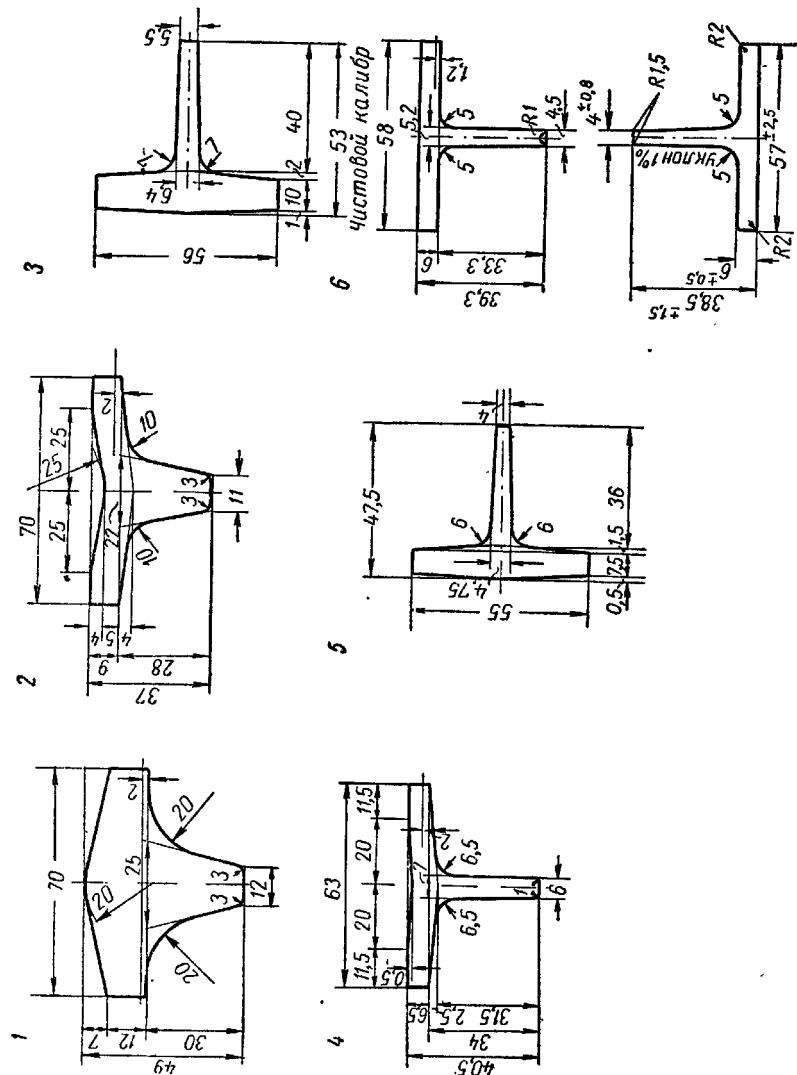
Размеры готового профиля и размеры шаблонов калибров при прокатке тавровой стали 57×38, 5×6×4 мм на стане 500:
